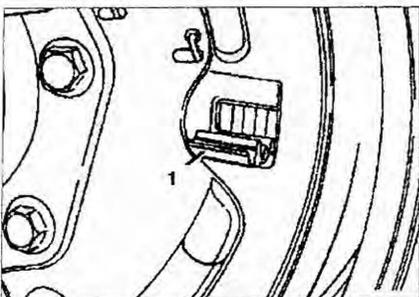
Проверьте толщину внутренней прокладки тормозной колодки барабанного тормозного механизма заднего колеса через отверстие в защитном кожухе, сняв предварительно пробки 1.
